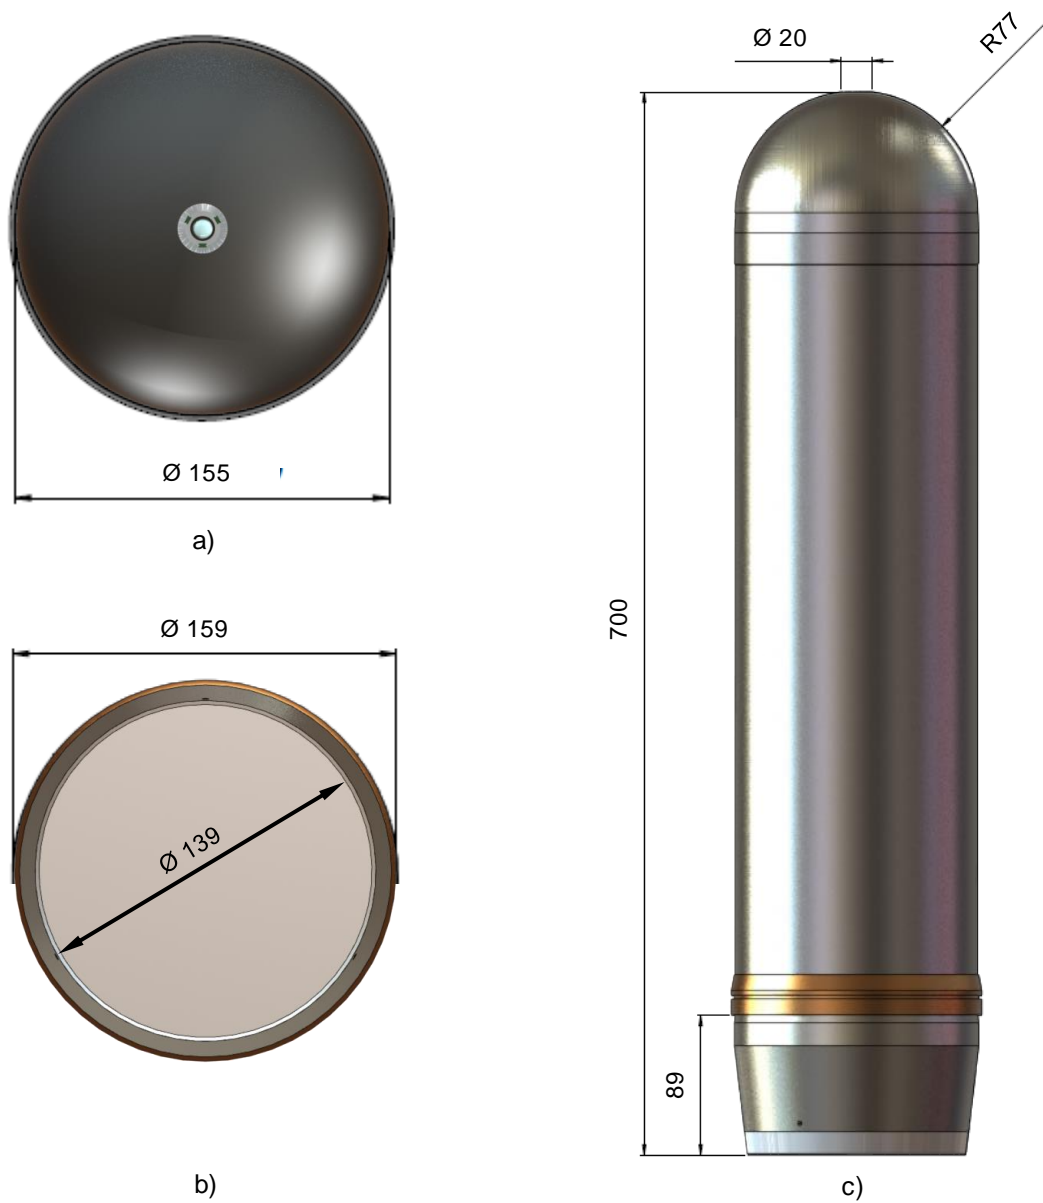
Cotas de atravancamento do projectil (em mm): a) Vista de baixo; b) Planta; c) Alçado principal
